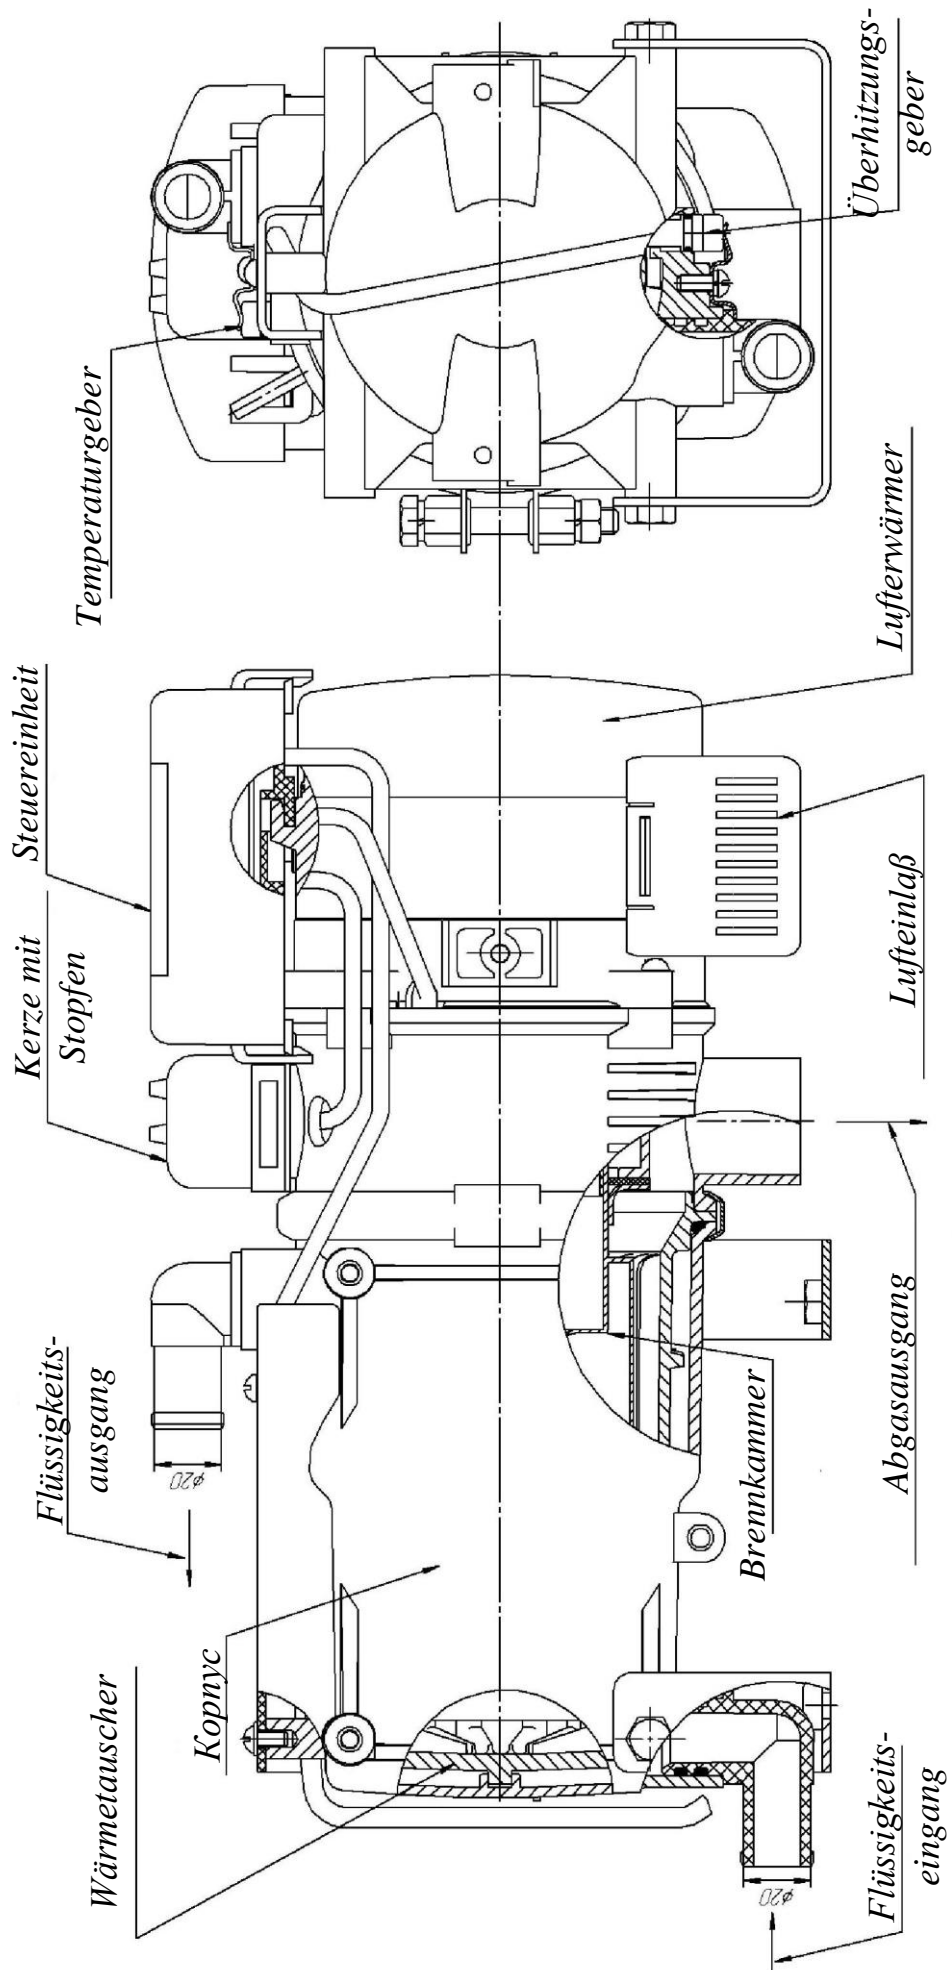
Hauptbaugruppen des Heizgerätes
